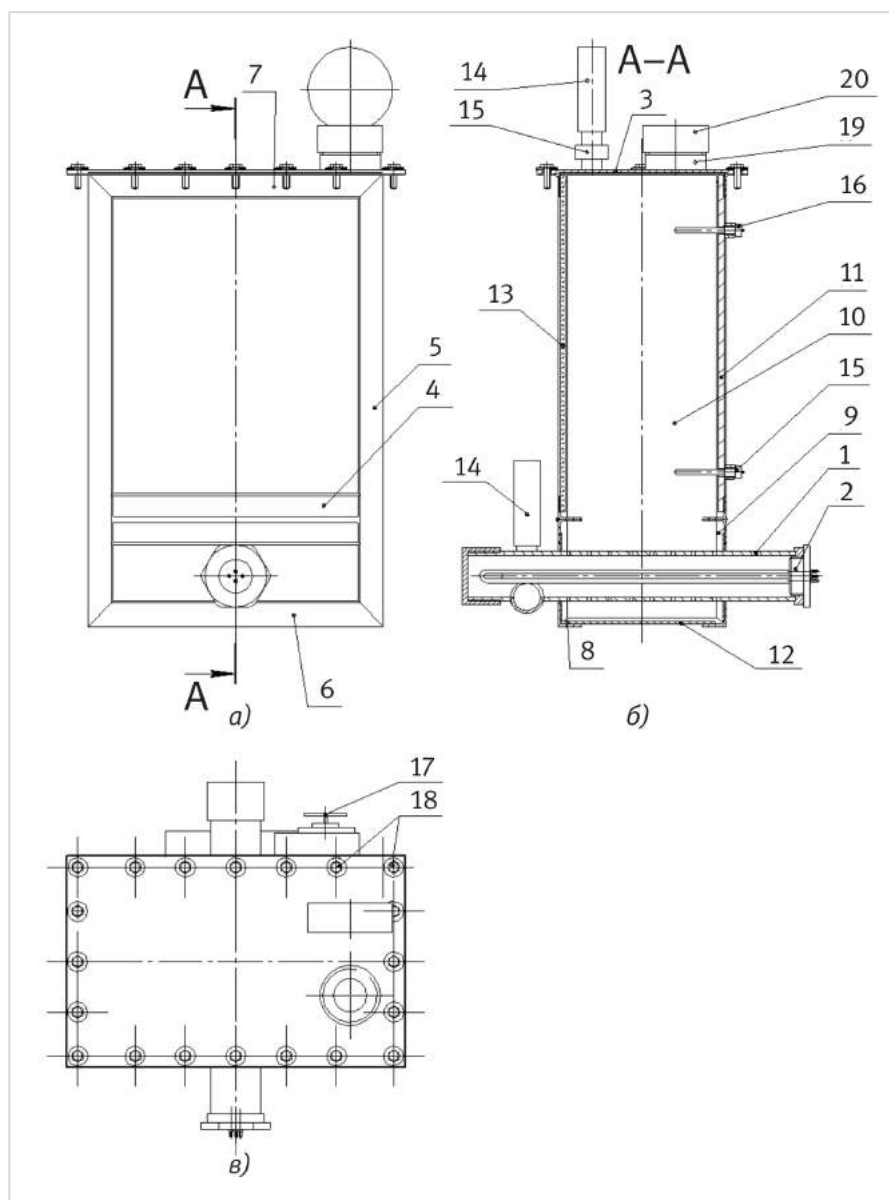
Вид стенда со стороны подключения нагревательного элемента (а), разрез А-А (б), вид сверху (в): 1 — перфорированный патрубок; 2 — нагревательный элемент; 3 — крышка; 4 — переключки; 5 — боковые уголки; 6 — передний и задний нижние уголки; 7 — передний и задний верхние уголки; 8 — верхние и нижние задние уголки; 9 — передняя и задняя нижние стенки с отверстиями; 10 — боковые стенки; 11 — задняя верхняя стенка; 12 — дно; 13 — термостойкое стекло; 14 — манометры; 15 — аварийный клапан; 16 — термодатчики; 17 — сливной кран; 18 — болты; 19 — горловина; 20 — пробка
